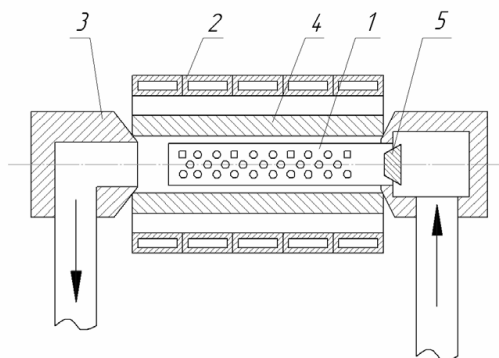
Схема восстановления наружного диаметра поршневого пальца термоупруго-пластическим деформированием: 1 – спрейер; 2 – индуктор; 3 – втулка; 4 – поршневой палец; 5 – гидроклапан
